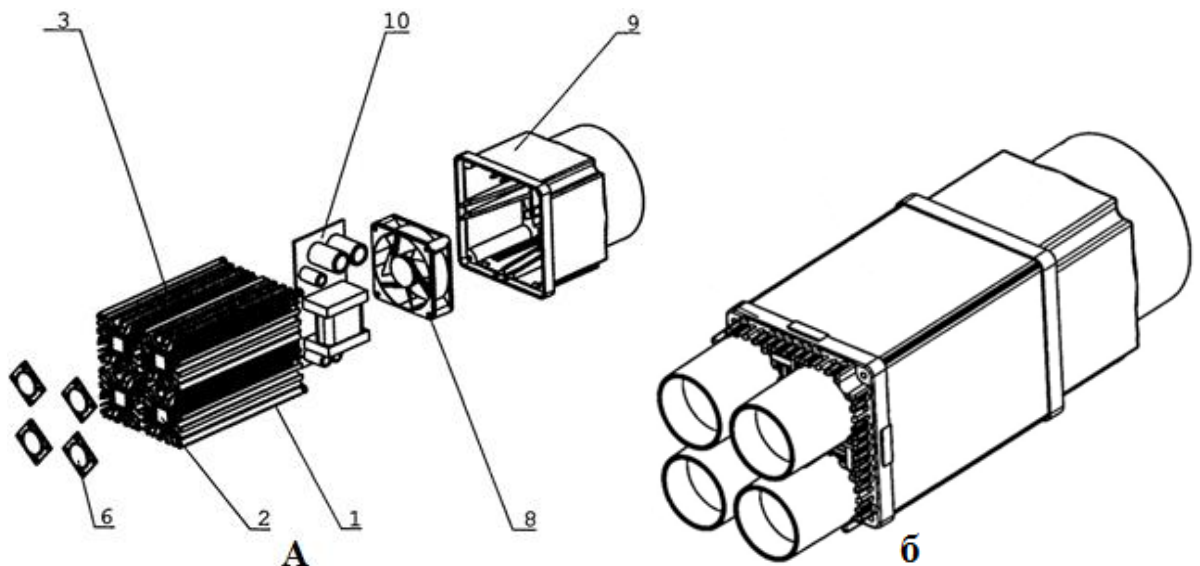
а) Компонентные части; б) Внешний вид светодиодного прожектора патента [5]
